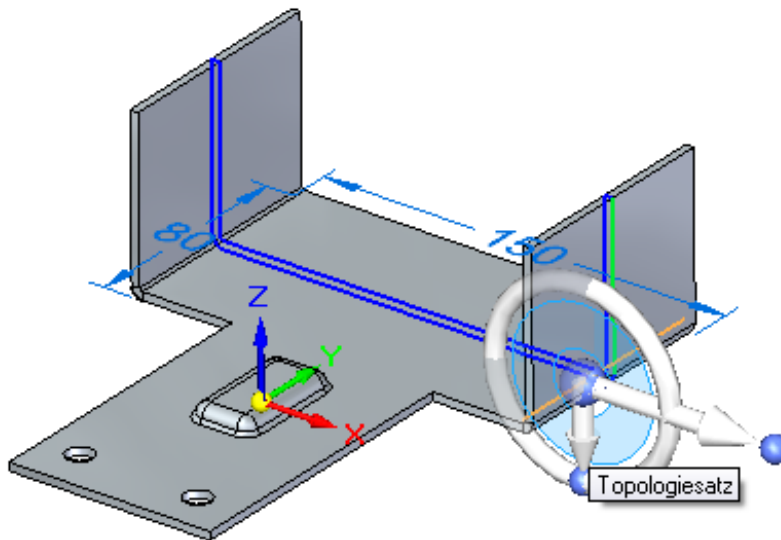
Steuerrad auf der Biegelinie platzieren
